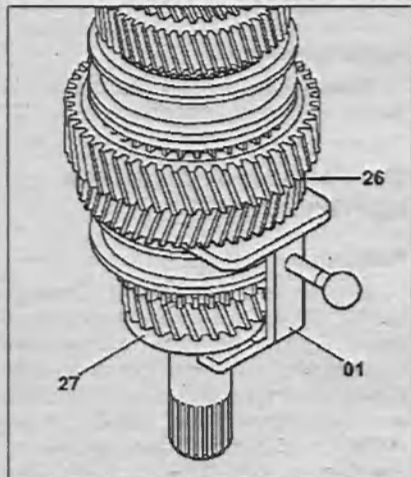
Установите фиксатор 01 кольца синхронизатора между шестерней 5-й передачи 26 и регулировочной прокладкой 27.
